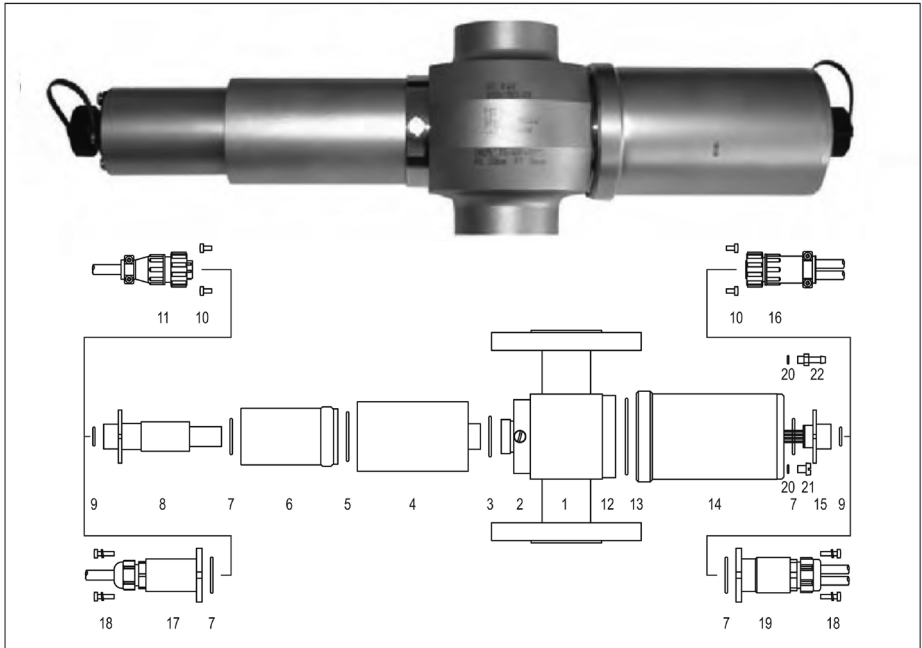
Foto e vista esplosa dell'unità TF56-N
